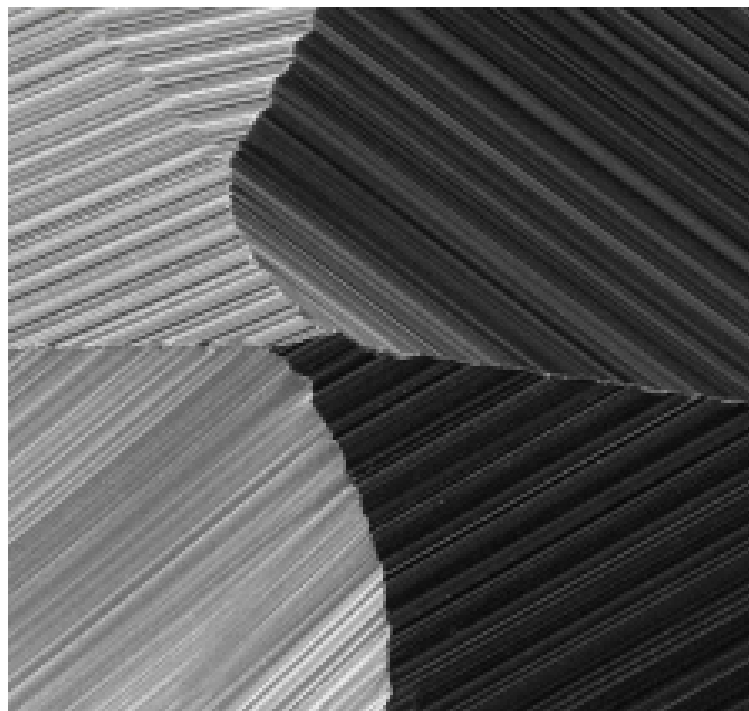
Поздовжня шорсткість ріжучих кромок свердла
